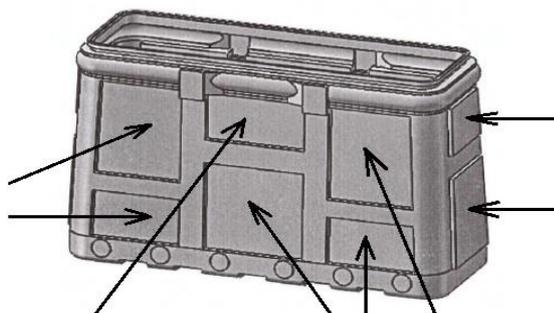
Корпус камеры КОТ-3-ССД, крышка снята. Стрелками показаны монтажные площадки на боковых и торцевых стенках корпуса.
